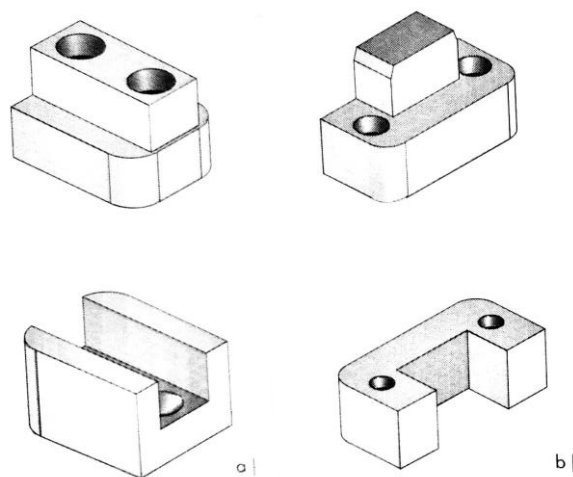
Exemplos de blocos de travamento: a) retangular tipo A; b) retangular tipo B.
